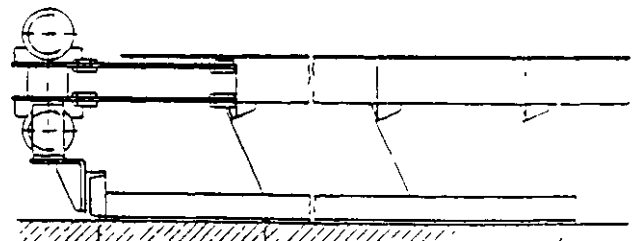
Lenkgeführte Förderrinne mit Aufspannung am Fundament
